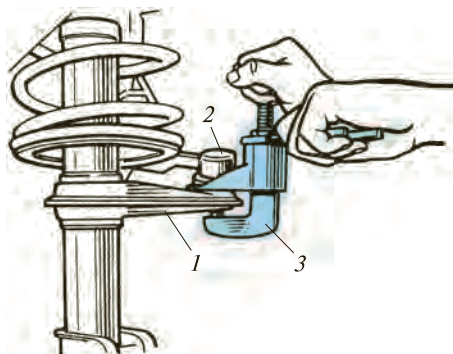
Выпрессовка пальца шарового шарнира рулевой тяги из поворотного рычага стойки по двески:
